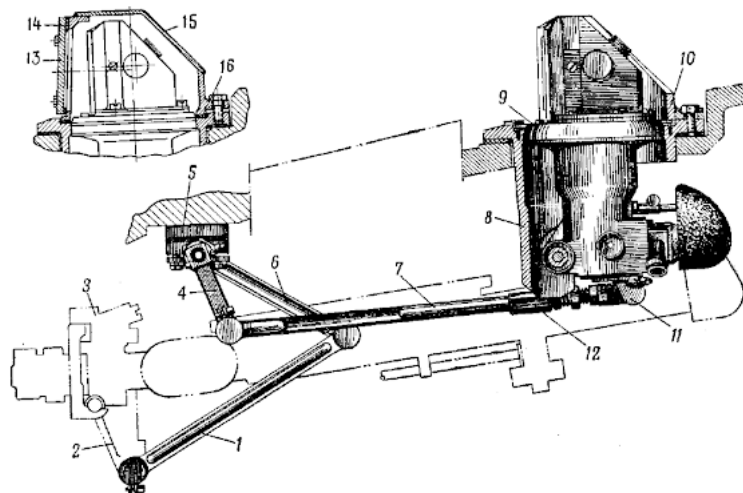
Установка прицела ТПН-1-41-11 в танке:
